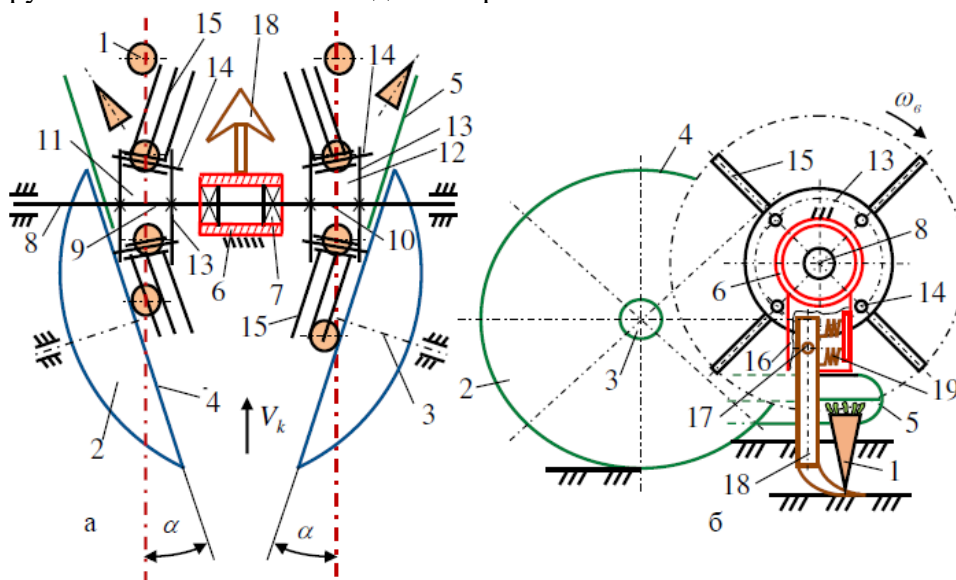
Конструктивна схема комбінованого копача: а – вигляд зверху; б – вигляд збоку
